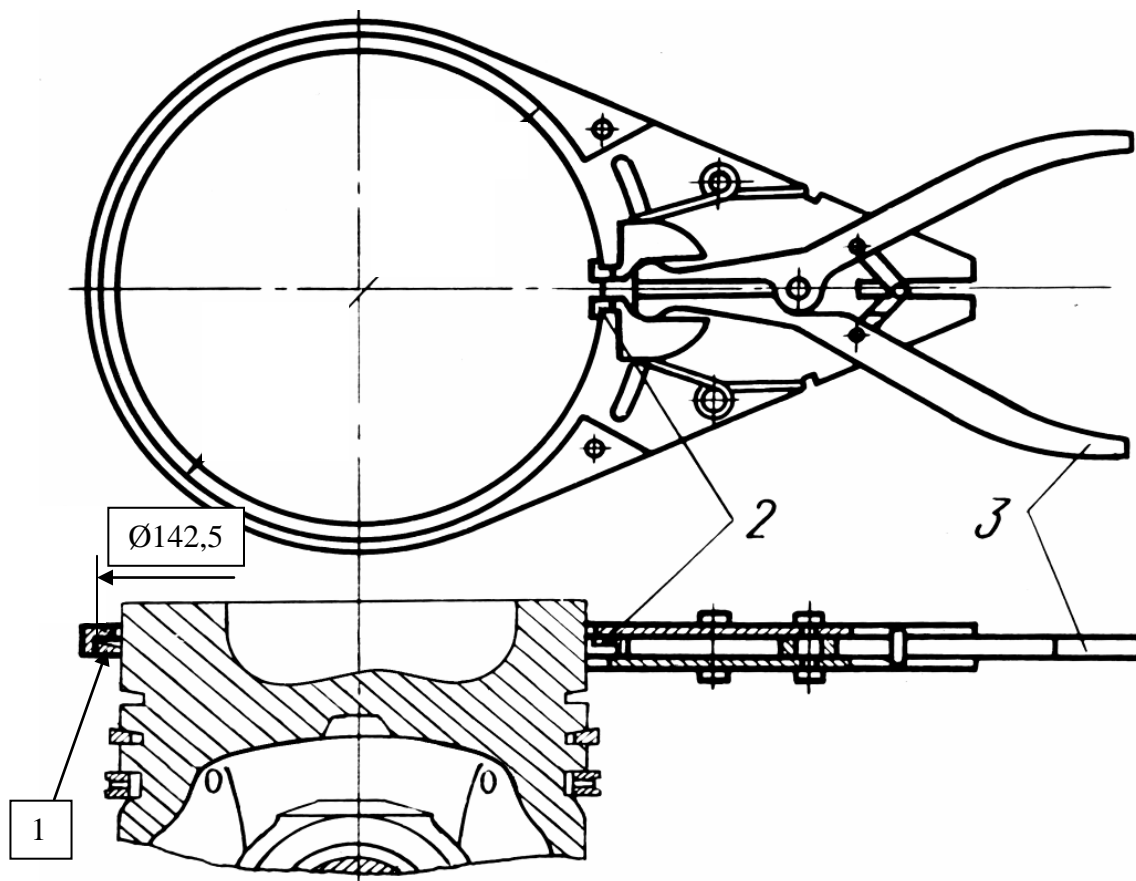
Приспособление для снятия и установки поршневых колец
